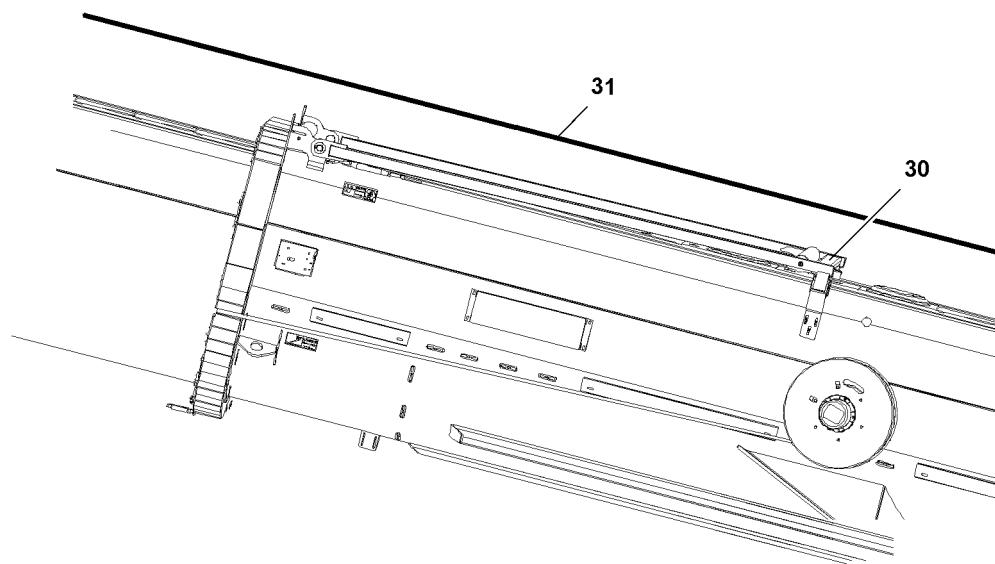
Recorrido del cable de elevación sobre el estribo del cable de elevación 30
